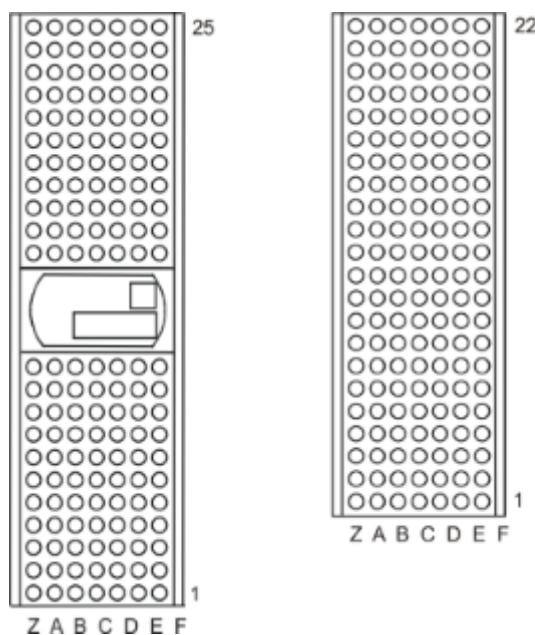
Steckverbinder P1 und P20 Front (Ansicht: Steckseite)
